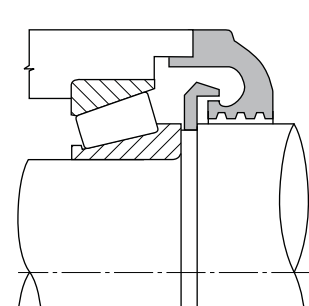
Gefräster schirmförmiger Schleuderteller in Verbindung mit umlaufenden Rillen und Metallring.
